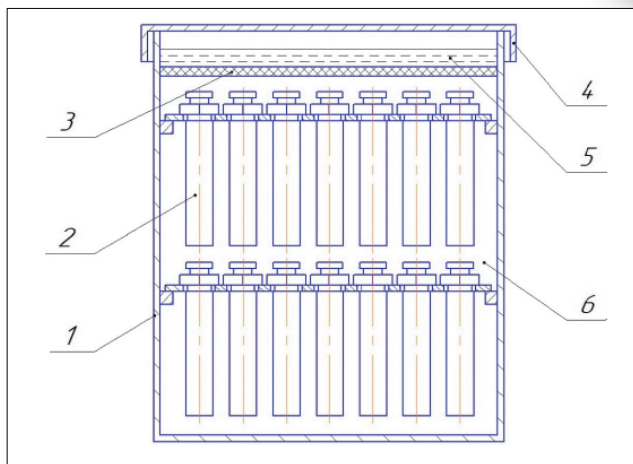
Схема упаковки контейнера: 1 – контейнер; 2 – плунжеры; 3 – прокладка асбестовая; 4 – крышка; 5 – затвор плавкий; 6 – смесь порошковая
